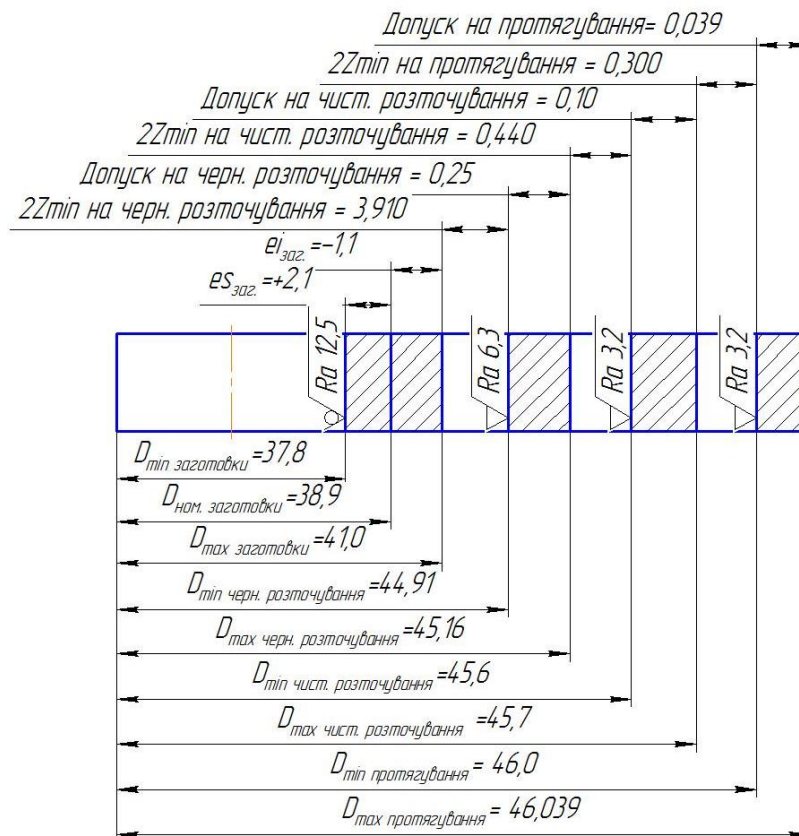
Схема розташування припусків і допусків розміру $\varnothing 46H8mm$
